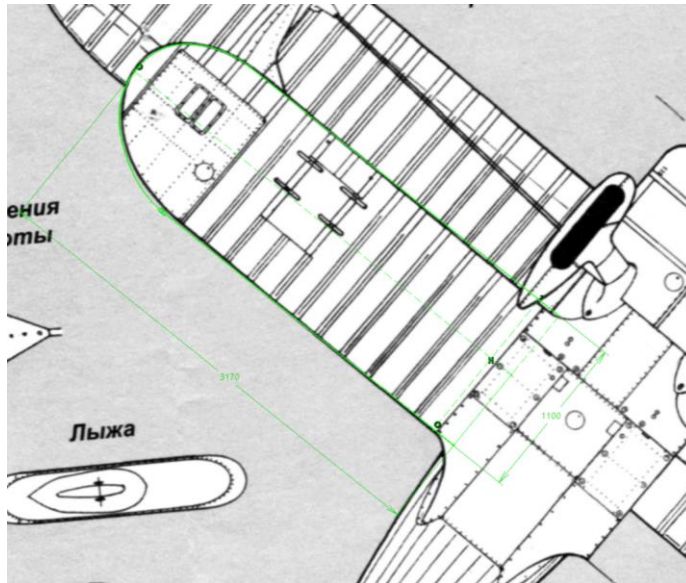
Sketch sobre el plano de la forma en planta del ala inferior
